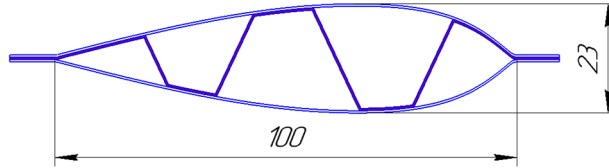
Поперечний переріз фрагменту металеві порожнистої лопатки
